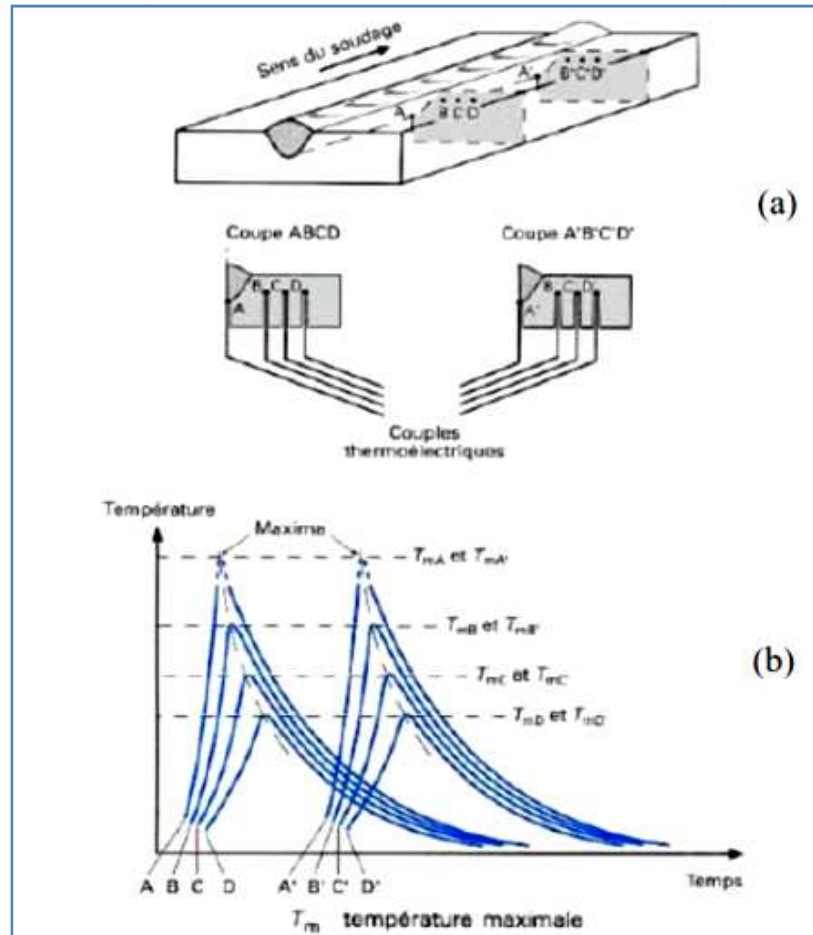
Cycles thermiques de soudage [20].
